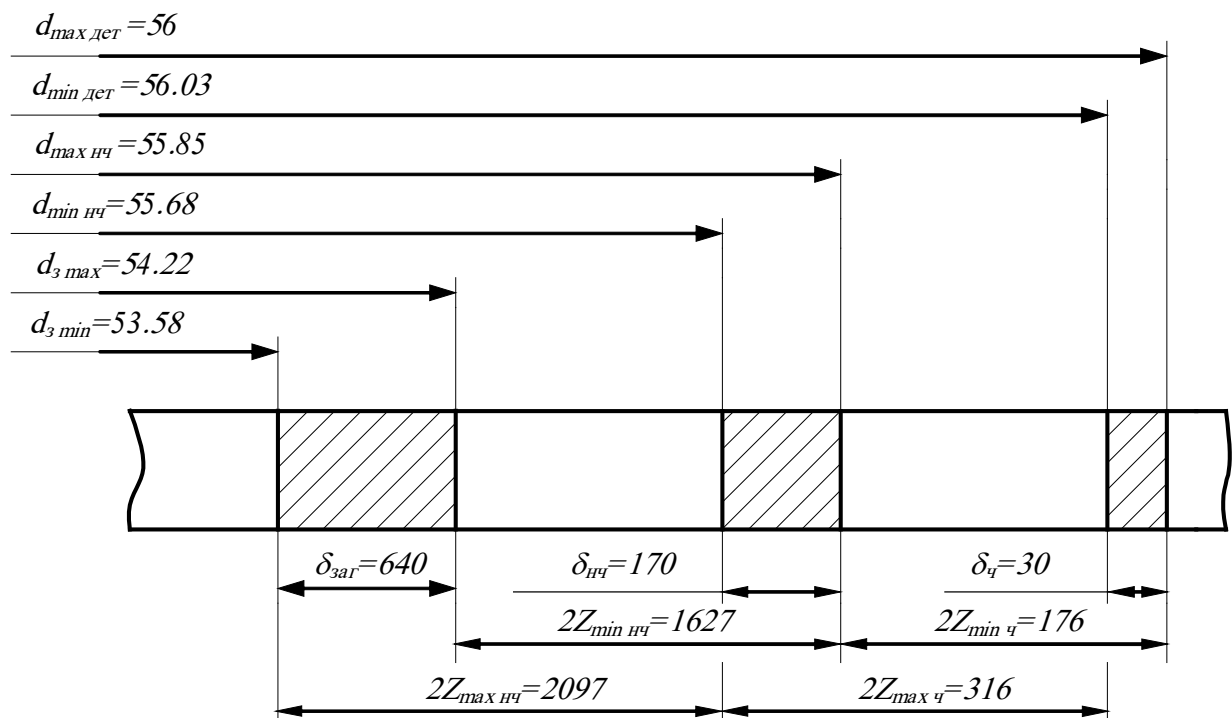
Припуски і допуски на поверхню $\varnothing 56H7$ гільзи установки моделі Кег Бой С2.
